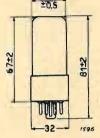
Dimensioni d in-gombro della valvola 6E5.
